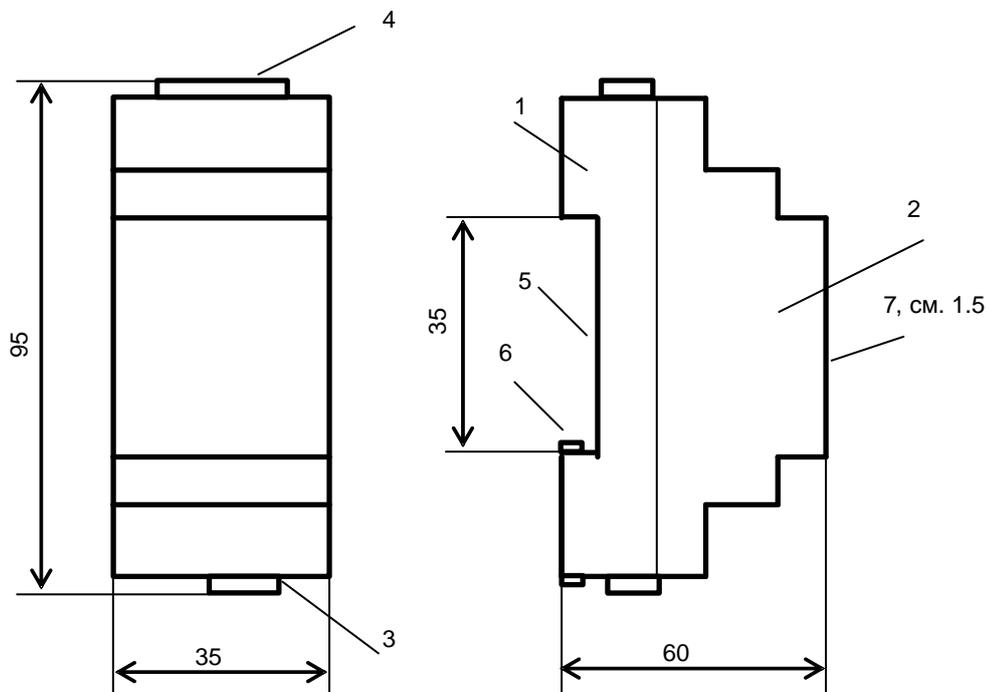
габаритные и установочные размеры устройства сопряжения
